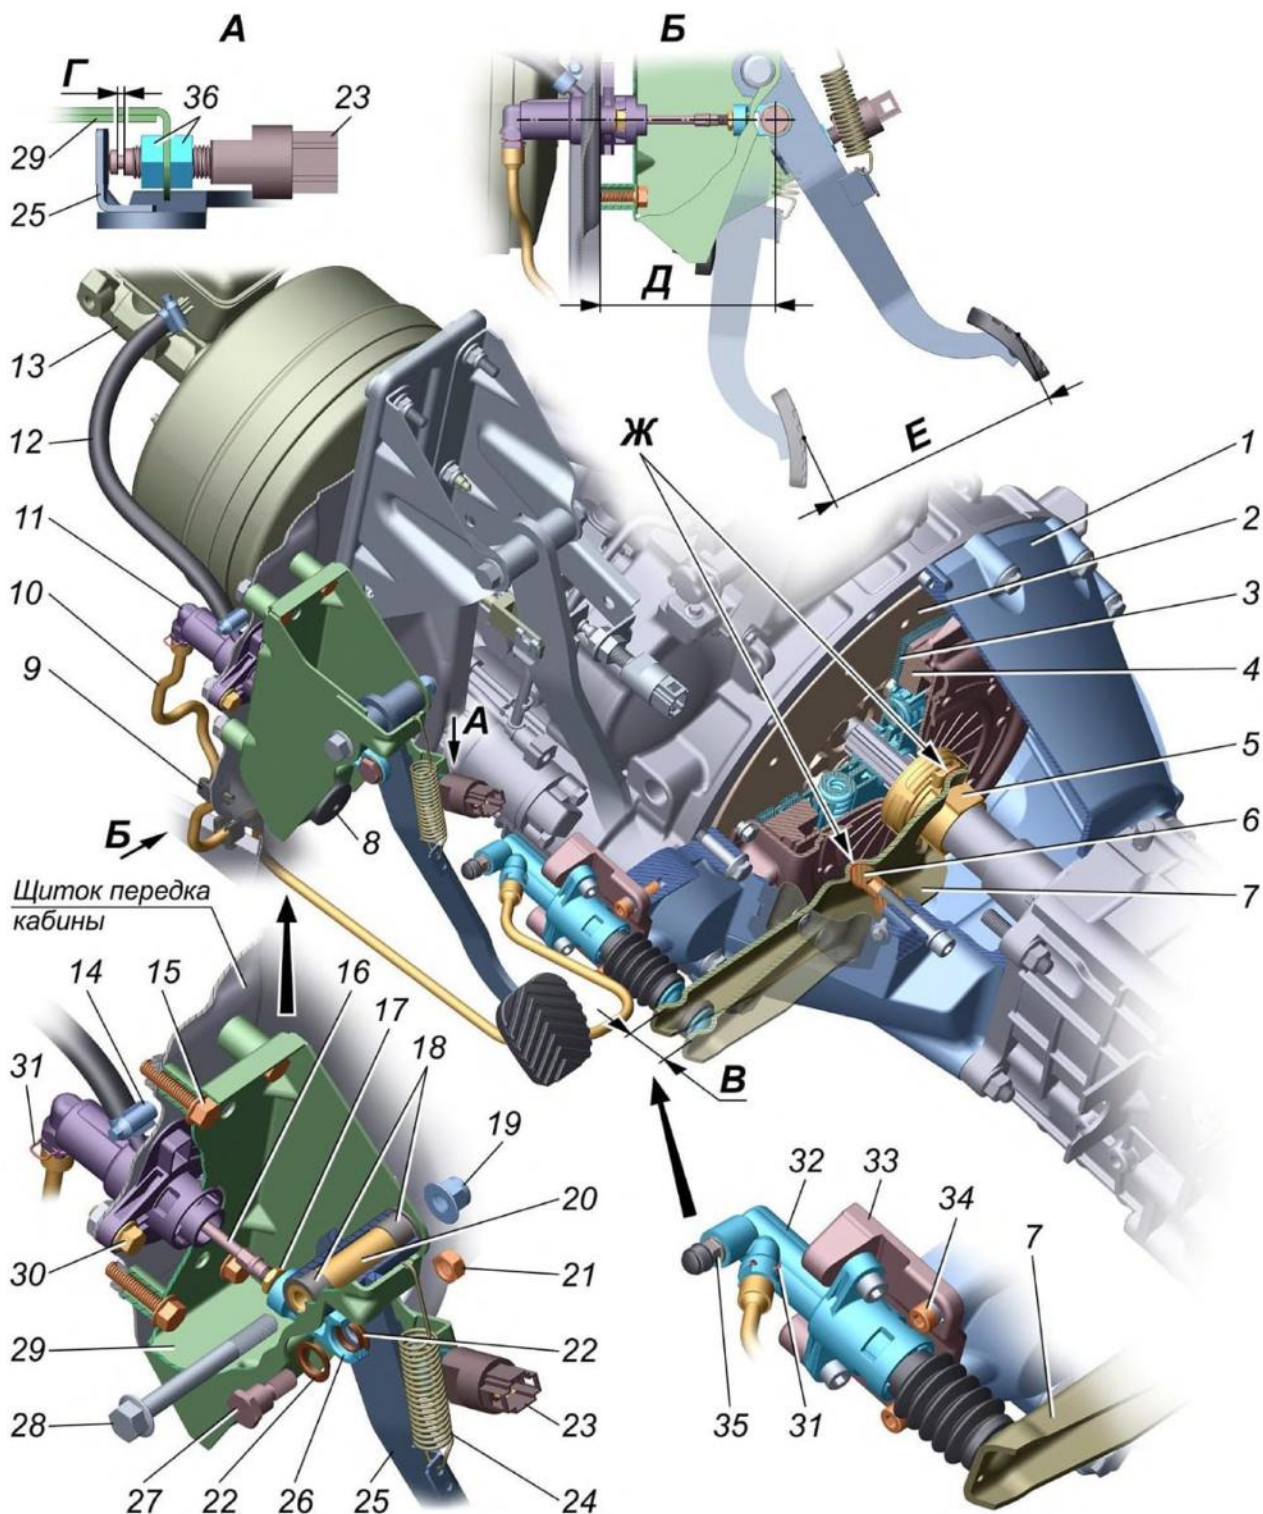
Сцепление и привод выключения сцепления: В- ход конца вилки выключения сцепления; Г - регулировочный размер выключателя сигнала положения педали сцепления; Д - установочный размер проушины толкателя; Е – ход педали сцепления; 1 - картер сцепления; 2 - маховик; 3 - ведомый диск; 4 - нажимной диск; 5 – муфта с подшипником; 6 - опора вилки включения сцепления; 7 - вилка; 8- буфер педали сцепления; 9,31- скобы; 10 - трубопровод; 11 - главный цилиндр сцепления; 12 - шланг; 13 – вакуумный усилитель с главным цилиндром тормозов и бачком; 14 – хомут; 15,28,30- болты; 16 - толкатель; 17,19,21,36- гайки; 18 – втулки оси педали; 20 – втулка распорная; 22 – втулки оси толкателя; 23 - выключатель сигнала положения педали сцепления; 24 – пружина; 25 - педаль сцепления; 26- проушина толкателя; 27 - ось толкателя педали; 29 - кронштейн педали сцепления; 32 - рабочий цилиндр сцепления; 33 - кронштейн; 34 –винт; 35 – клапан прокачки
